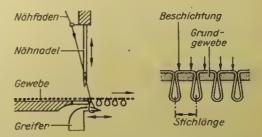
Werkzeuge einer Tuftingmaschine (links), Erzeugnisstruktur (rechts)
